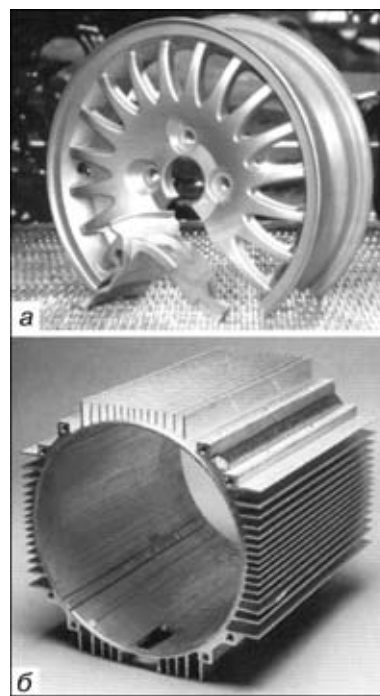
Автомобильный диск (а) и корпус электродвигателя (б), полученный СТП
